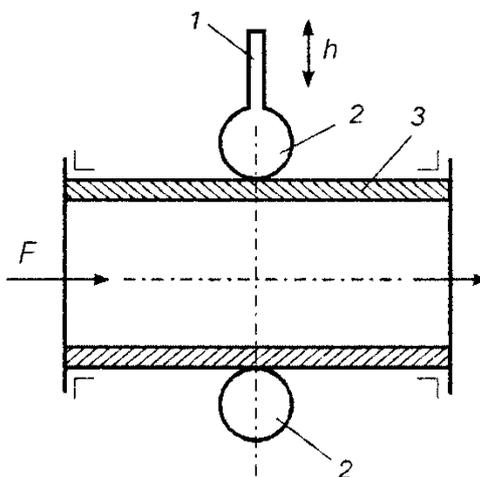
Шланговый регулирующий орган: 1 – шток; 2 – валики-траверсы; 3 – эластичный патрубок
